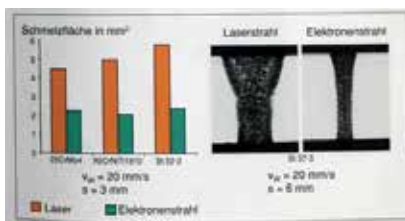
Поперечное сечение шва при лазерной и электронно-лучевой сварке [8].
